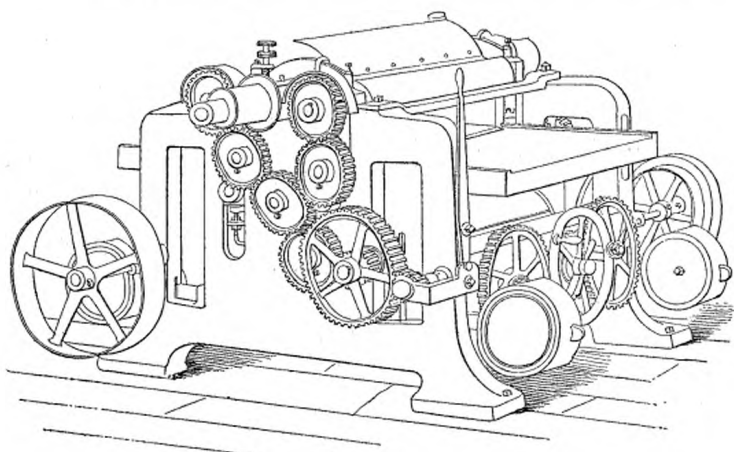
Machine à raboter n° 4 de la Egan Company.
